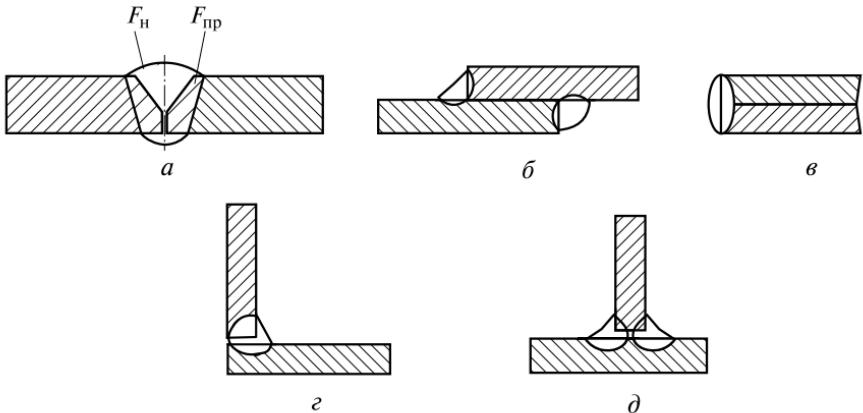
Схемы поперечного сечения стыкового (*а*), нахлесточного (*б*), торцового (*в*), углового (*г*) и таврового (*д*) сварных соединений:
